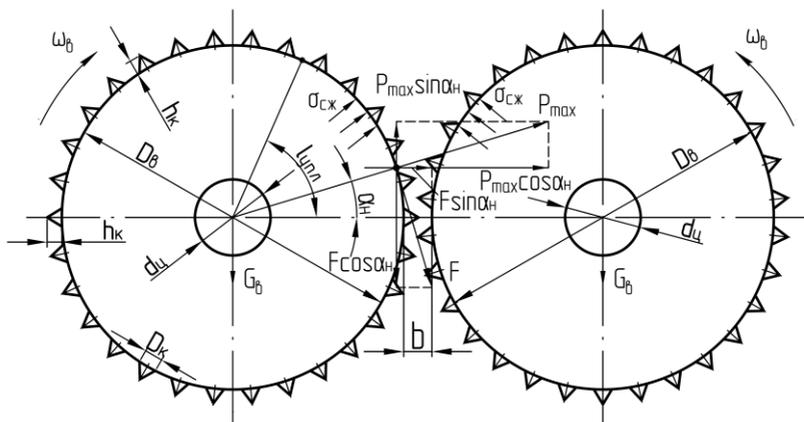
Схема для расчёта основных параметров пресс-валкового уплотнителя
